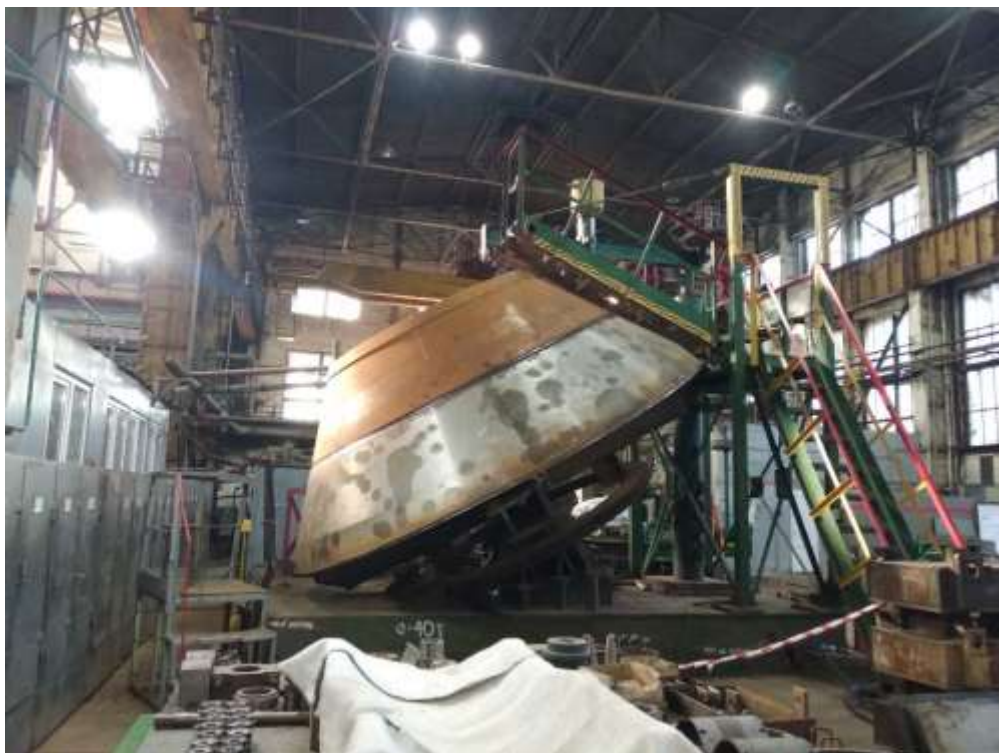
Підготовка до наплавлення конусу ЗАДП
